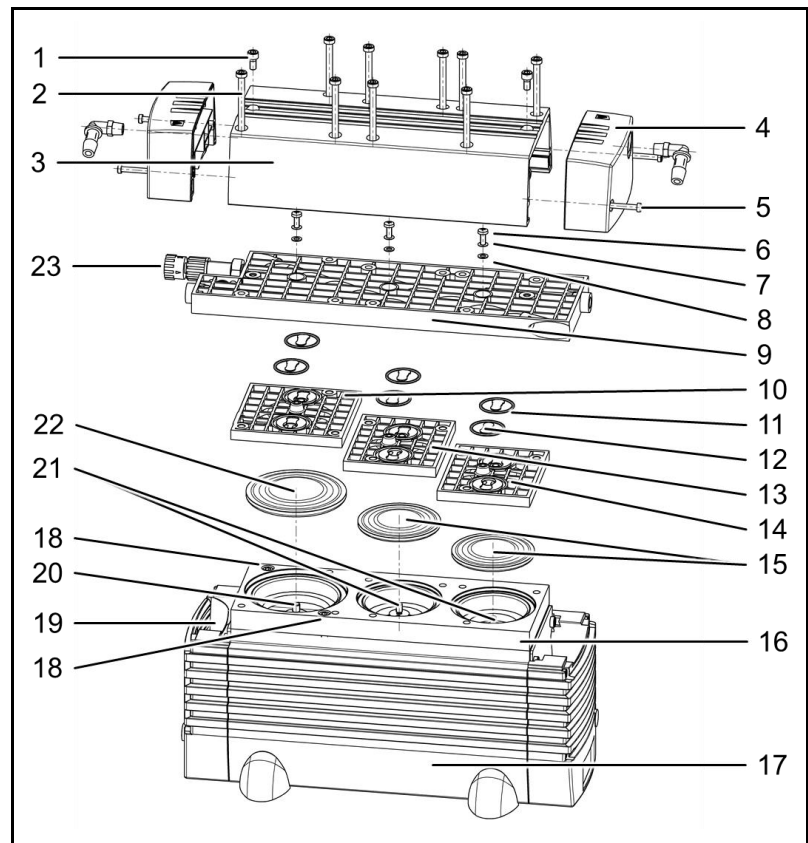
Pumpe (Explosionszeichnung, symbolisch)
